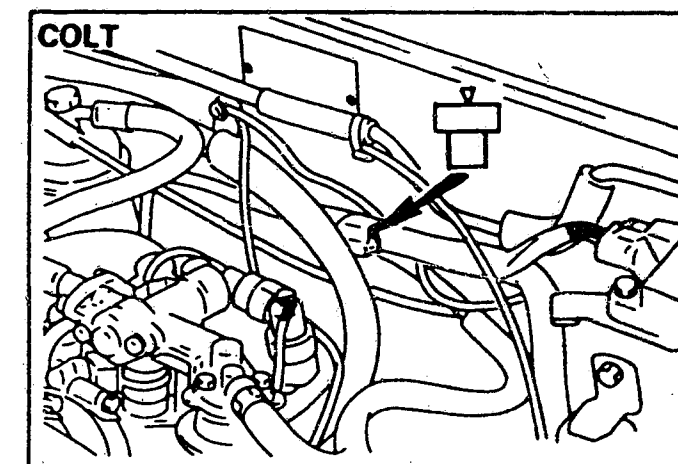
Lage des Diagnosesteckers im Motorraum beim Colt.
